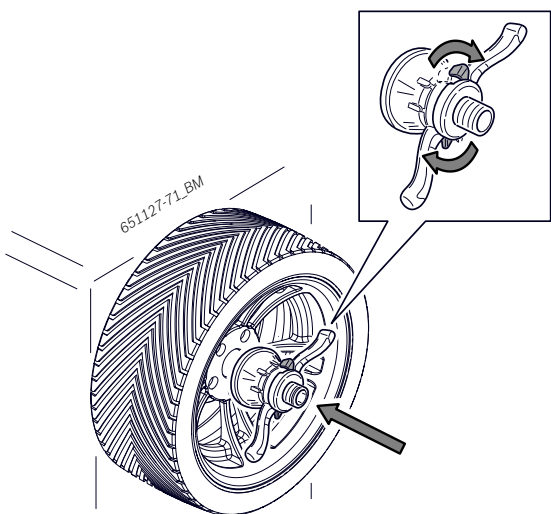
Positionner l'écrou à serrage rapide déverrouillé sur l'arbre
